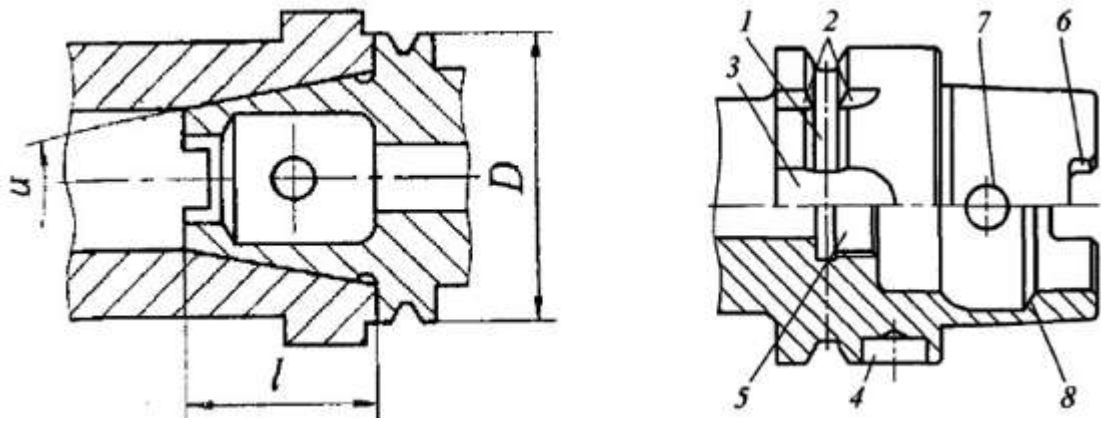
Оправки HSK для верстатів з ЧПУ
